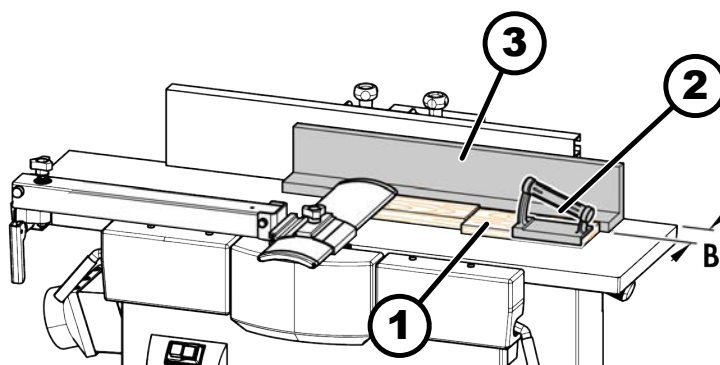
Ceillado - Mecanizado de piezas pequeñas
